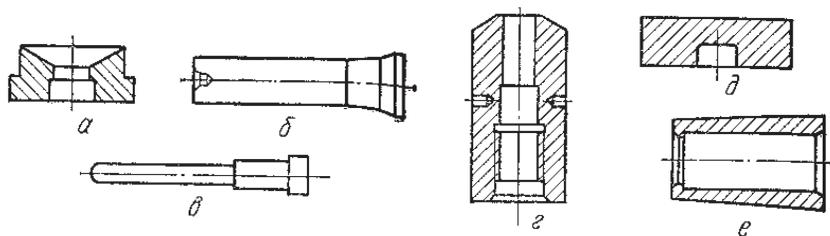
Инструмент для прессования: а – матрица; б – пуансон; в – игла; г – иглодержатель; д – пресс-шайба; е – втулка контейнера
